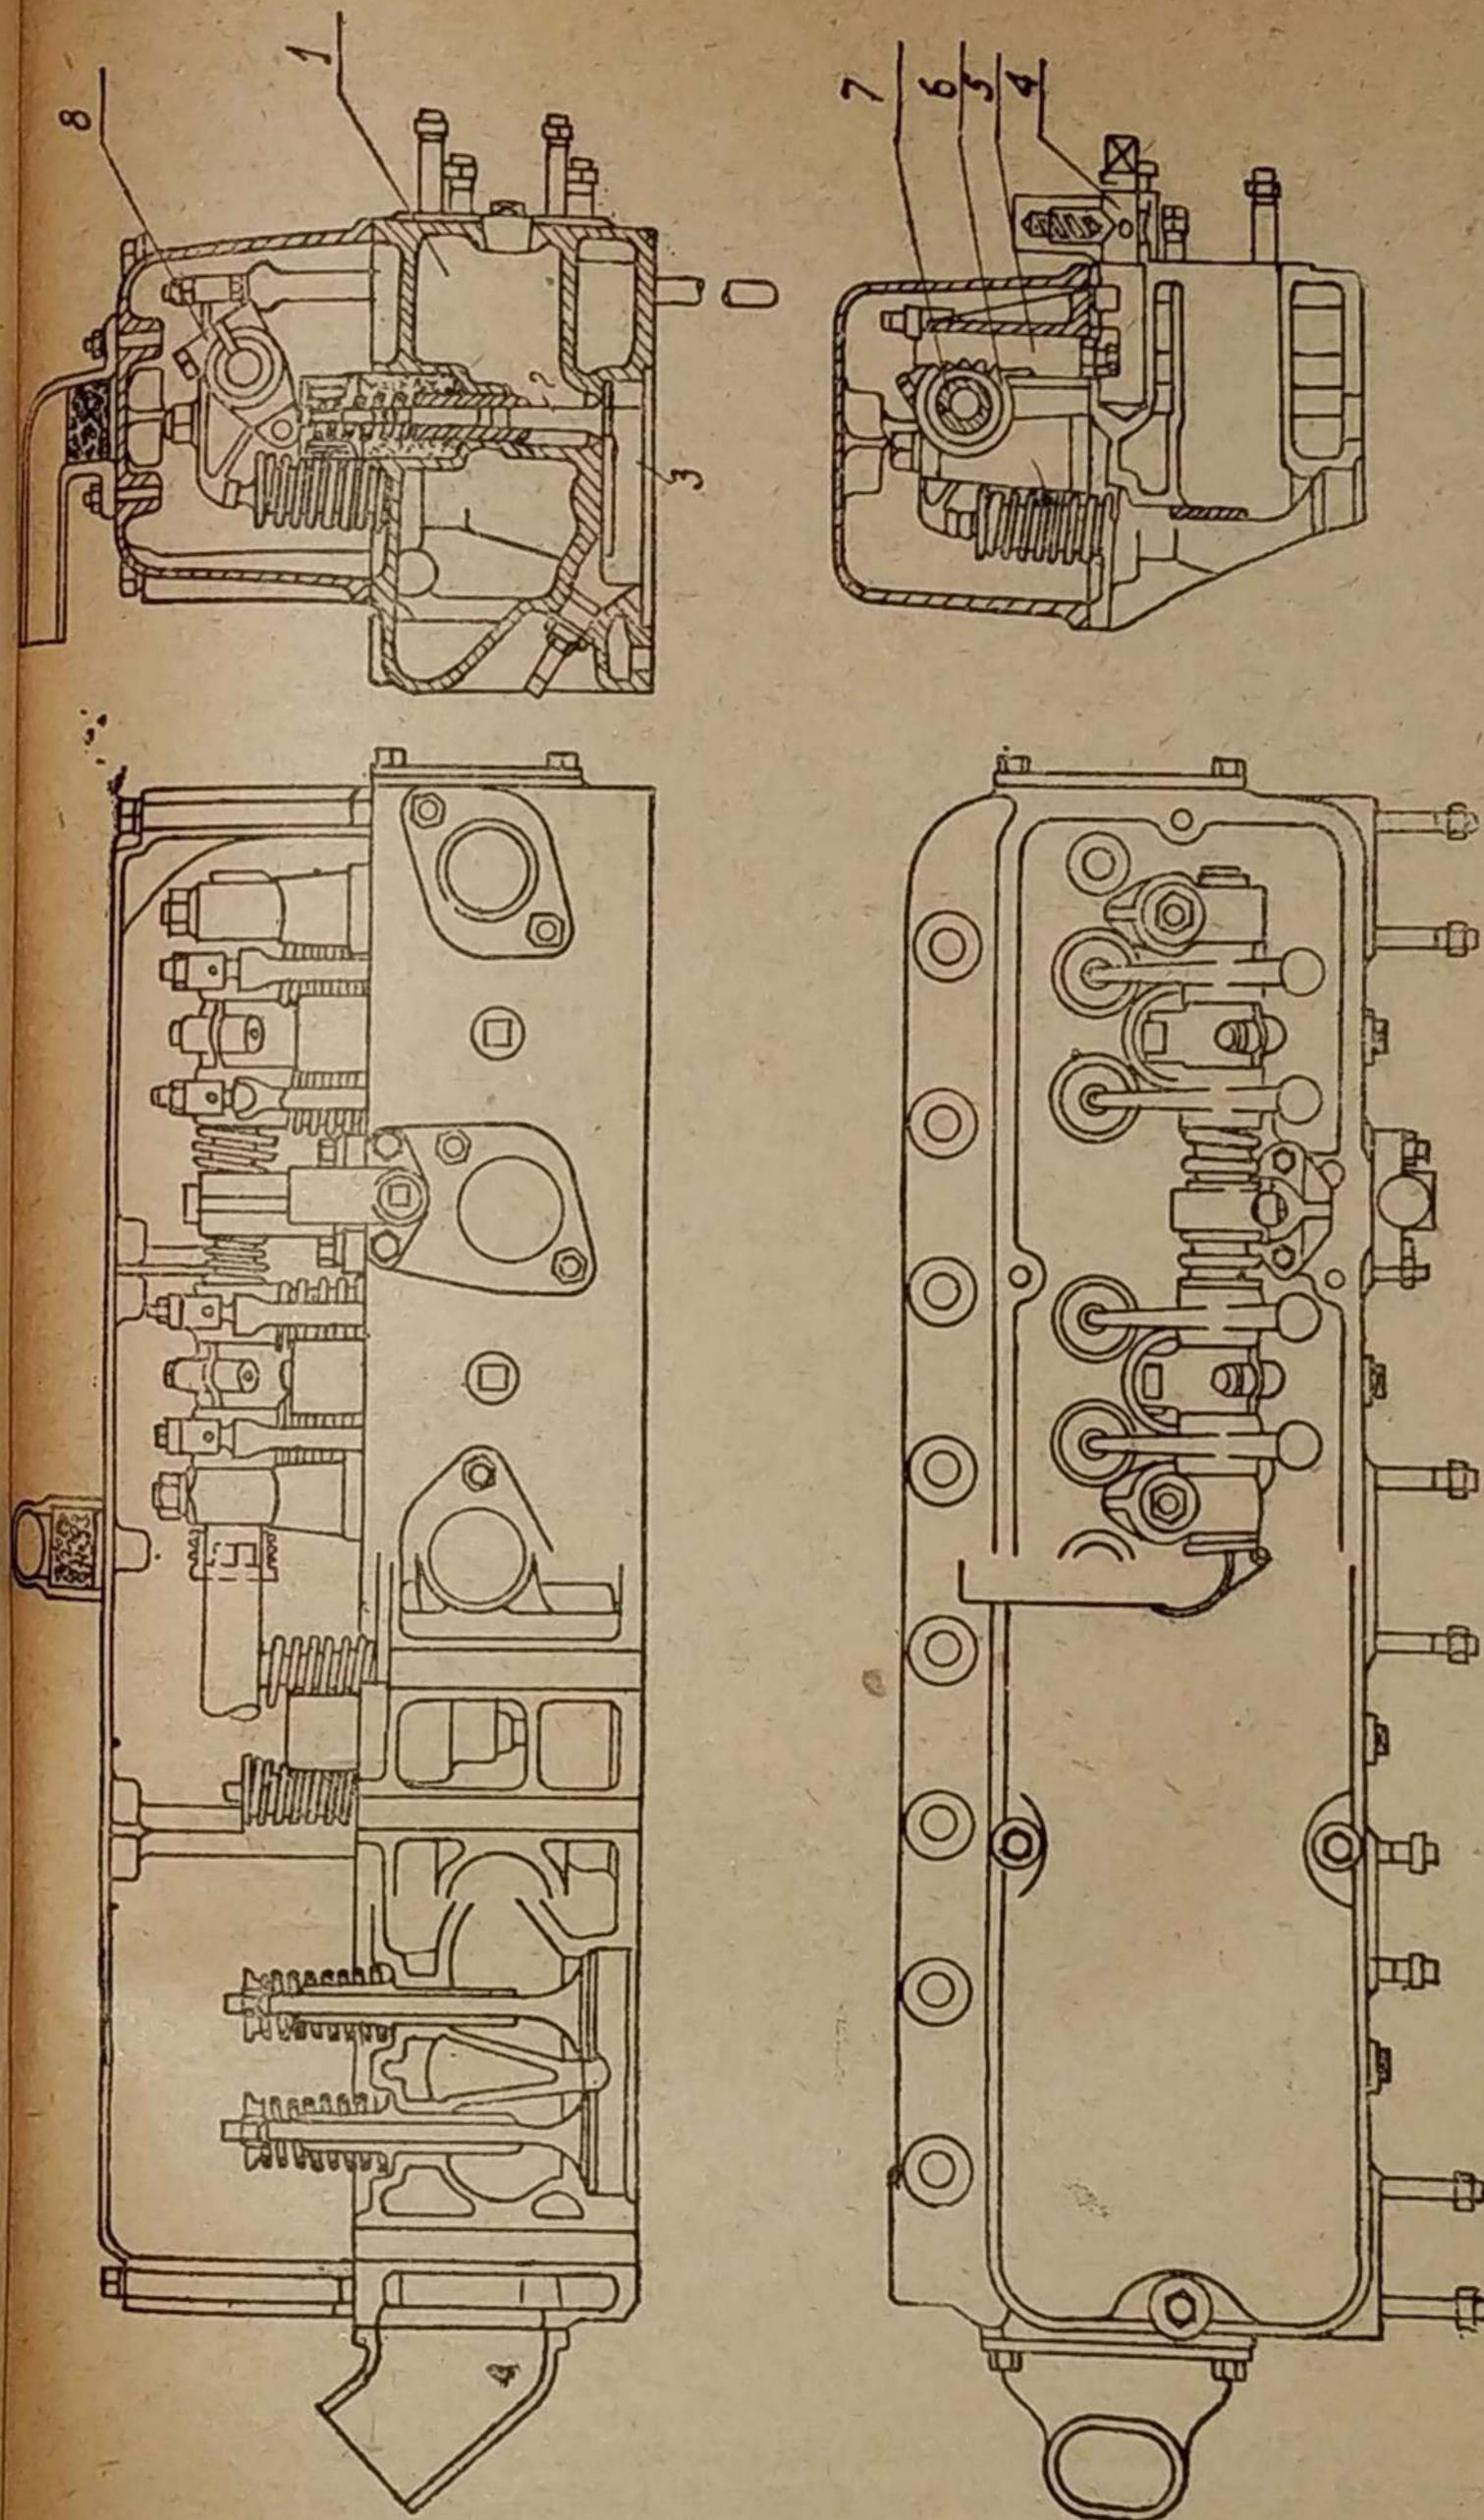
Головка цилиндров двигателя ХТЗ «Д-2Г»
